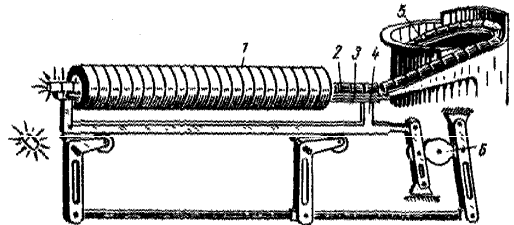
Схема методического нагревателя с цилиндрическим индуктором и шагающим механизмом для транспортирования заготовок:
